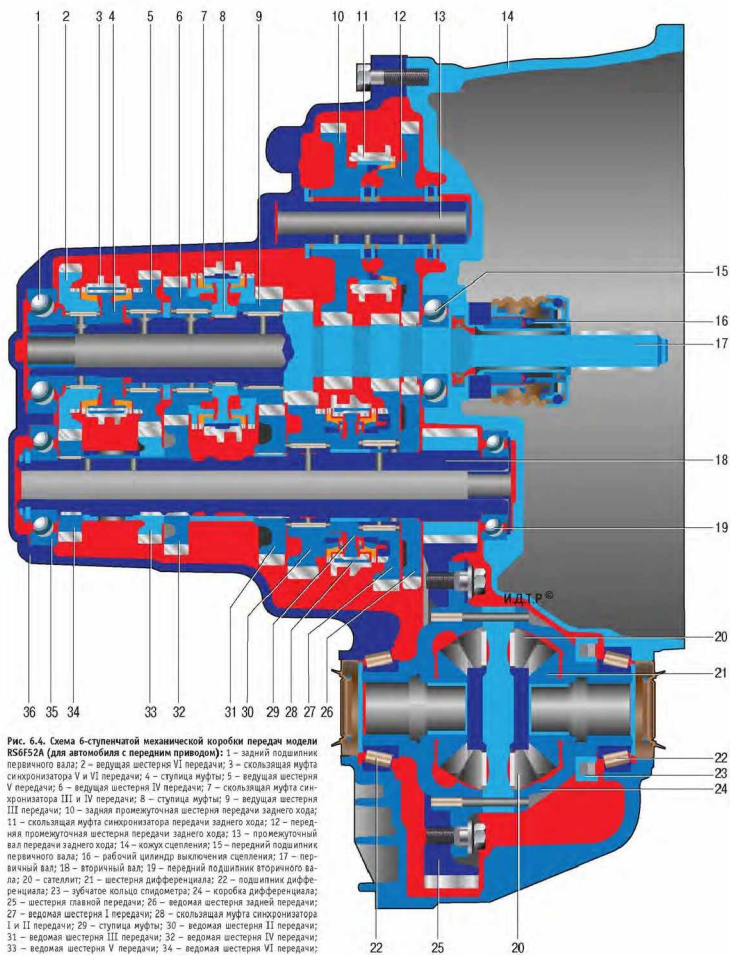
Схема 6-ступенчатой механической коробки передач модели RS6F52A (для автомобиля с передним приводом): 1 – задний подшипник первичного вала; 2 – ведущая шестерня VI передачи; 3 – скользящая муфта синхронизатора V и VI передачи; 4 – ступица муфты; 5 – ведущая шестерня V передачи; 6 – ведущая шестерня IV передачи; 7 – скользящая муфта синхронизатора III и IV передачи; 8 – ступица муфты; 9 – ведущая шестерня III передачи; 10 – задняя промежуточная шестерня передачи заднего хода; 11 – скользящая муфта синхронизатора передачи заднего хода; 12 – передняя промежуточная шестерня передачи заднего хода; 13 – промежуточный вал передачи заднего хода; 14 – кожух сцепления; 15 – передний подшипник первичного вала; 16 – рабочий цилиндр выключения сцепления; 17 – первичный вал; 18 – вторичный вал; 19 – передний подшипник вторичного вала; 20 – сателлит; 21 – шестерня дифференциала; 22 – подшипник дифференциала; 23 – зубчатое кольцо спидометра; 24 – коробка дифференциала; 25 – шестерня главной передачи; 26 – ведомая шестерня задней передачи; 27 – ведомая шестерня I передачи; 28 – скользящая муфта синхронизатора I и II передачи; 29 – ступица муфты; 30 – ведомая шестерня II передачи; 31 – ведомая шестерня III передачи; 32 – ведомая шестерня IV передачи; 33 – ведомая шестерня V передачи; 34 – ведомая шестерня VI передачи; 35 – задний подшипник вторичного вала; 36 – картер коробки передач
